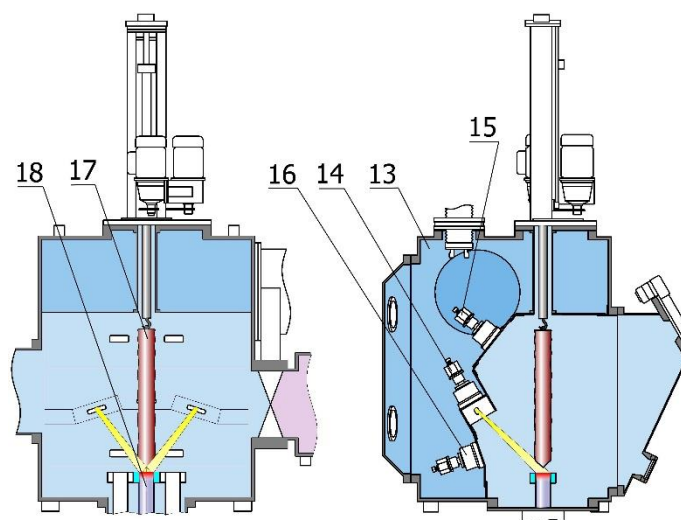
Схема переплаву заготовки безпосередньо в тигель: а - вид спереду; б - вид збоку (13 - камера гармат; 14 - гармати для переплавки і випаровування матеріалів; 15 - гармати для нагріву виробів зверху; 16 - гармати для нагріву виробів знизу; 17 - заготовка, що переплавляється; 18 - тигель і зливоч, що формується)
